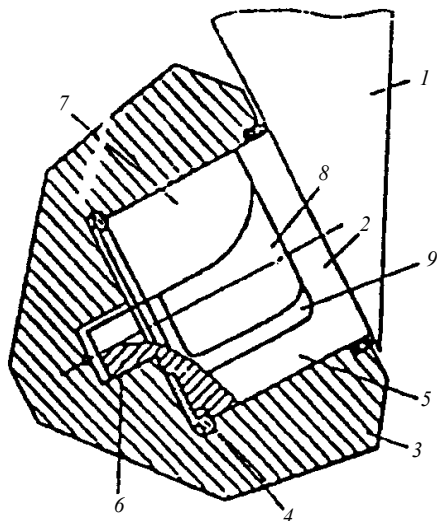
Конструкция опоры шарошечного долота (А. с. 1465534 А1 от 15.03.89): 1 – лапа; 2 – цапфа; 3 – шарошка; 4 – стопорное кольцо; 5, 6 – большой и малый подшипники скольжения; 7 – карман; 8 – вырезы боковые; 9 – переход выреза по ходу вращения ролика
